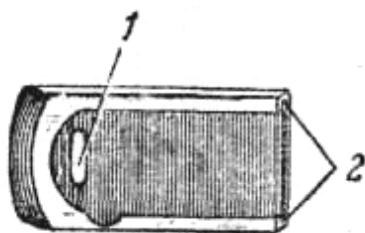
Крышка магазина: 1 – отверстие; 2 – пазы
